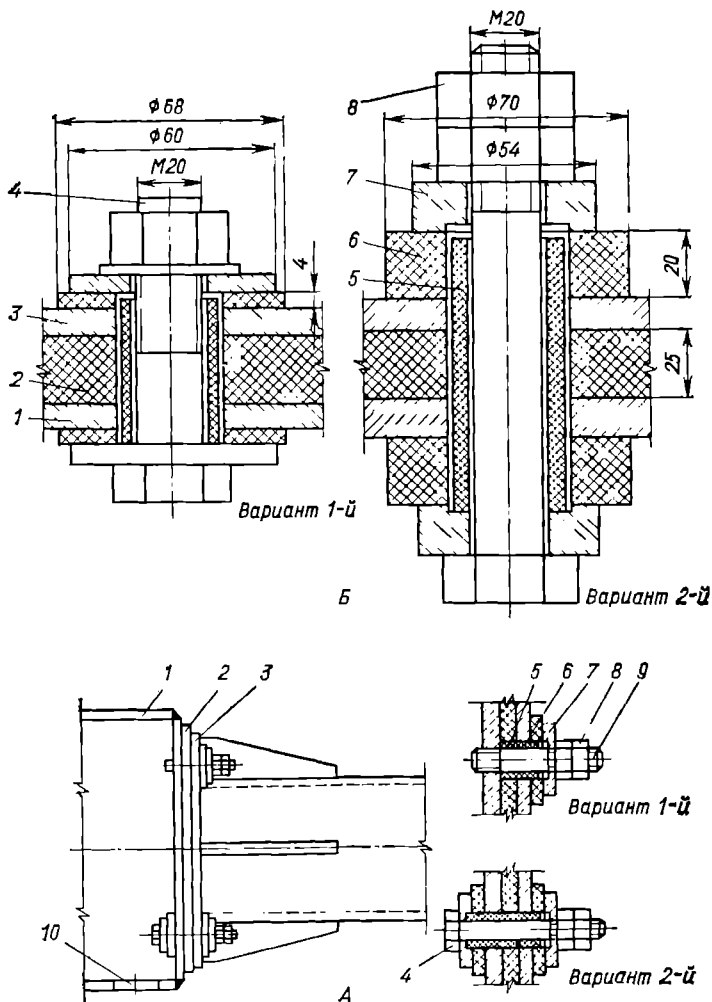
Примеры конструктивных решений узлов электрической изоляции: А — крепление фланца цилиндра к каретке дуговой сталеплавильной печи; Б — детальный разрез узла изоляции с болтовой стяжкой; 1 — конструкция заземленная; 2 — изоляционная плита; 3 — конструкция под напряжением; 4 — болт; 5 — изоляционная трубка; 6 — изоляционная шайба; 7 — специальная металлическая шайба; 8 — гайка; 9 — шпилька; 10 — окно для монтажа
